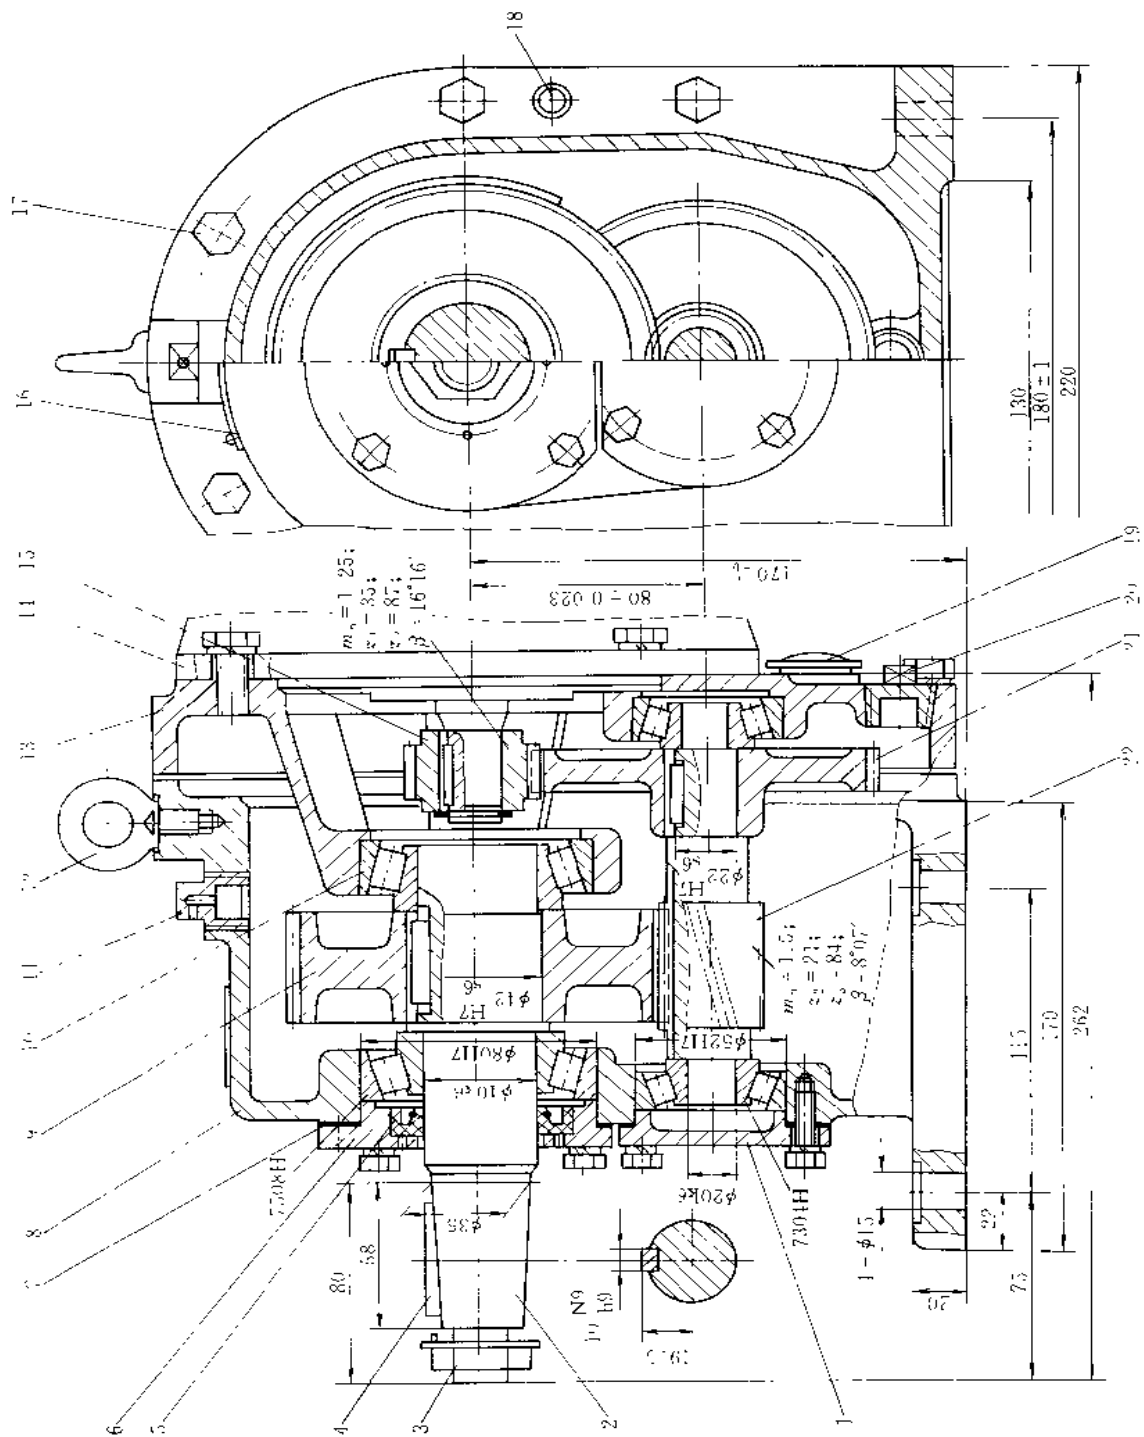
两级同轴式电机直联圆柱齿轮减速器
